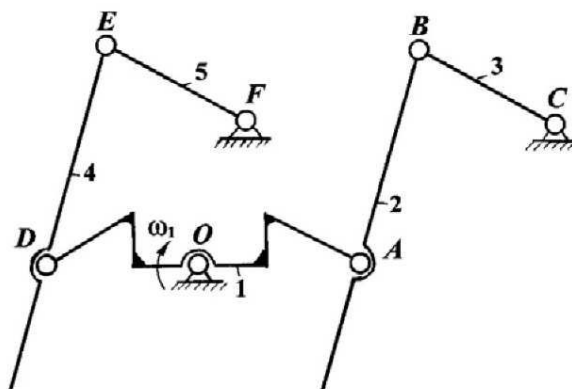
Механизм привода упаковщика пресс-подборщика
